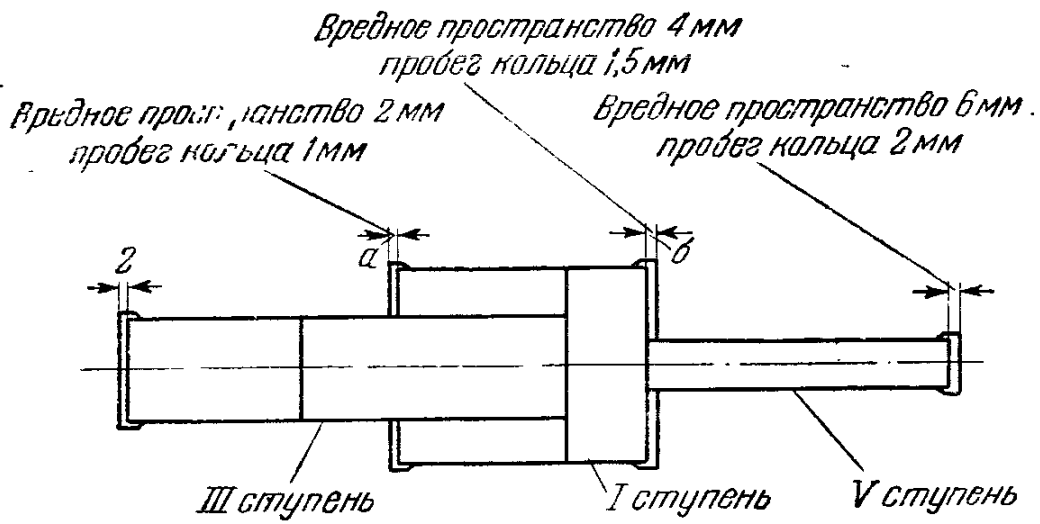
Установка поршней в цилиндрах двухлинейного компрессора.
